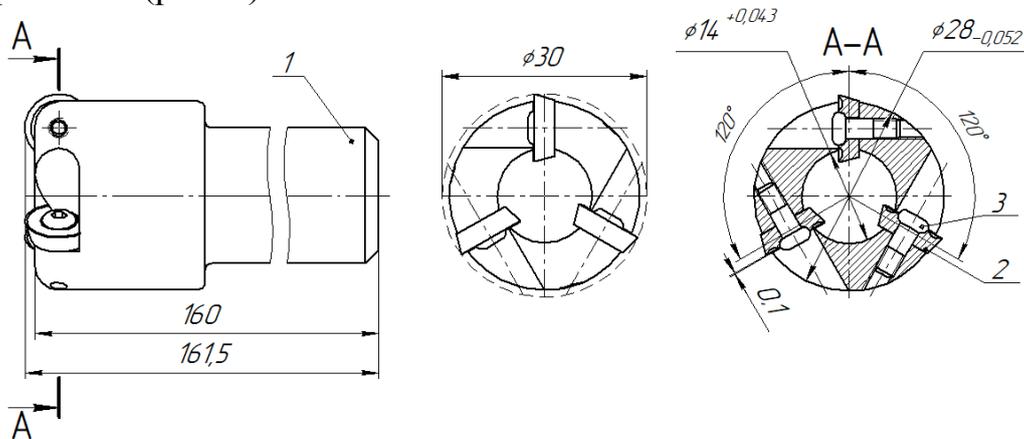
Фрагмент сборочного чертежа корпуса концевой фрезы:
